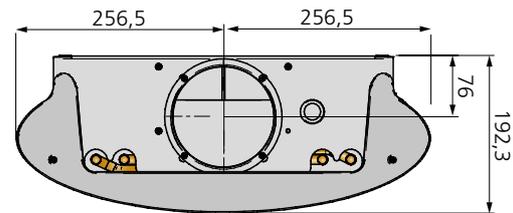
Dimensions ADRIATIC Ellips, vue arrière du raccordement aéraulique
